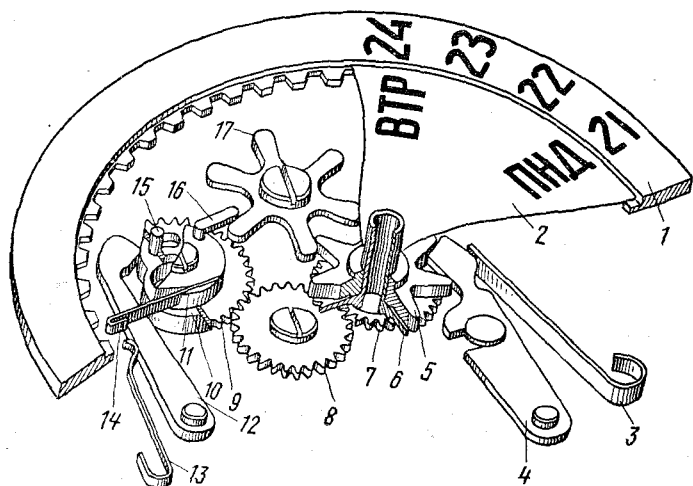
Кинематическая схема двойного календаря мгновенного действия:
